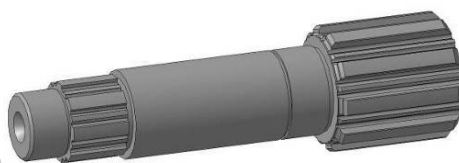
Пример конструкции вала коробки скоростей
